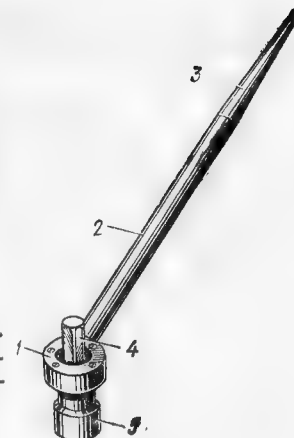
1 — головка корпуса; 2 — ручка; 3 — клин; 4 — головка (входной вал); 5 — головка сменная (выходной вал)
